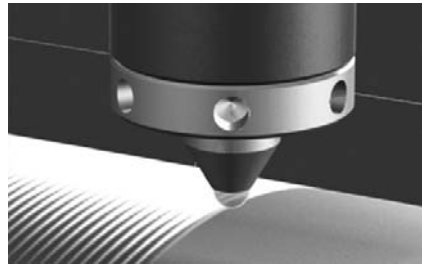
Rollieren mit einem Diamant-Glättwerkzeug [112]
